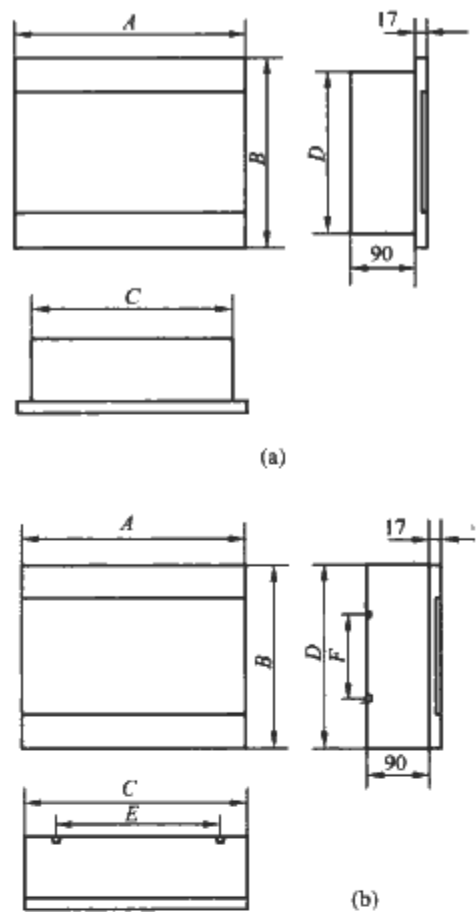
PZ36 的外形及安装尺寸图 (mm)
